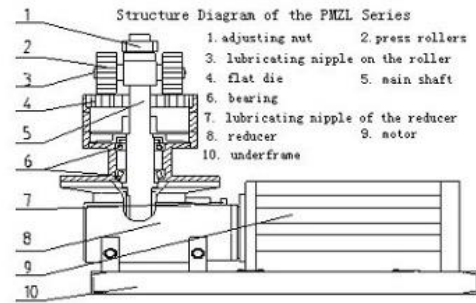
Мобільний завод з виготовлення пелет (Mobile Pellet Plant) [18]
